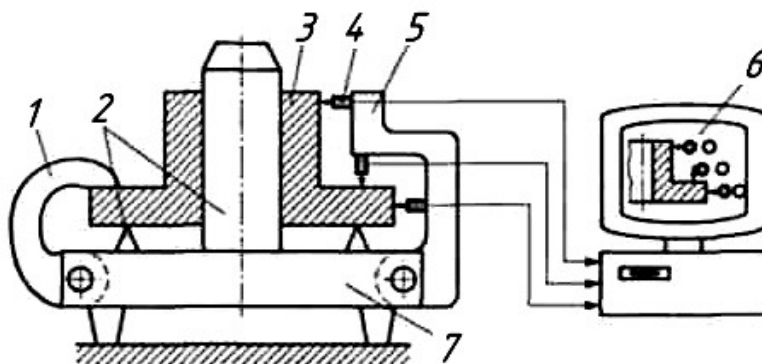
Приспособление для контроля размеров отливок: 1 – прижим; 2 – базовые поверхности; 3 – отливка; 4 – датчик размера; 5 – кронштейн; 6 – мнемосхема; 7 – основание
